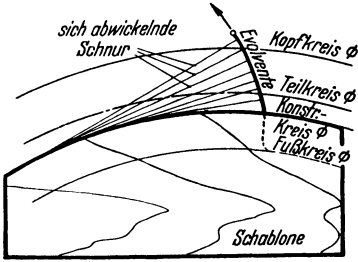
Genaue Evolvente, mittels Schnur aufzuzeichnen.
